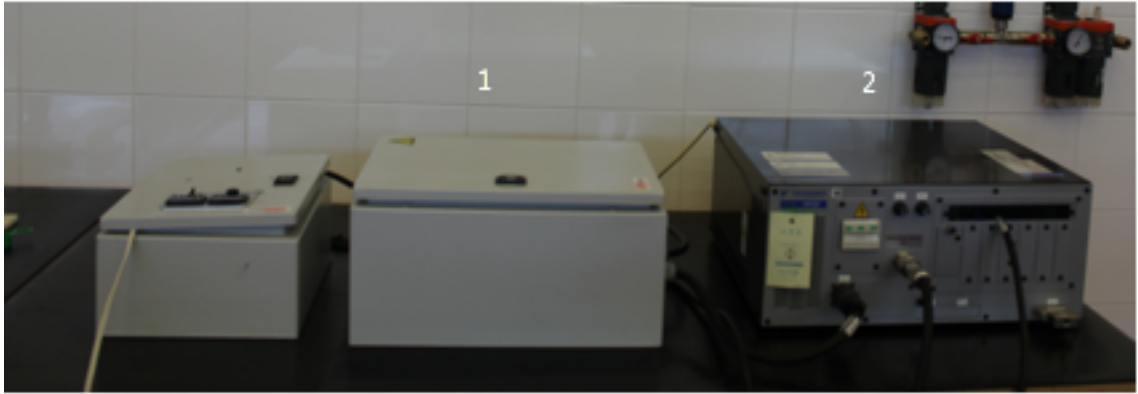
Controlo do equipamento (1- caixa de controlo do equipamento de soldadura; 2 - Processador do braço robot)
